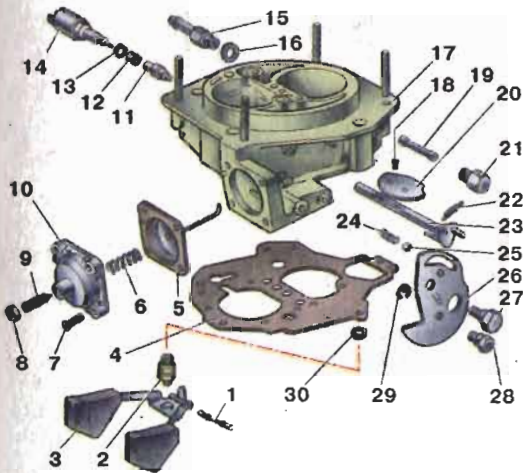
Детали крышки карбюратора мод. 2108: 1 – ось поплавков; 2 – топливный клапан; 3 – поплавок; 4 – прокладка крышки карбюратора; 5 – диафрагма пускового устройства; 6, 22, 24 – пружины; 7 – винт крепления крышки пускового устройства; 8 – контргайка; 9 – винт регулировки пускового зазора воздушной заслонки; 10 – крышка пускового устройства; 11 – топливный жиклер системы холостого хода; 12 – уплотнительное кольцо электромагнитного клапана; 13 – обойма уплотнительного кольца; 14 – электромагнитный клапан; 15 – штуцер подачи топлива; 16, 30 – уплотнительные шайбы; 17 – крышка карбюратора; 18 – винт крепления воздушной заслонки; 19 – топливный фильтр; 20 – воздушная заслонка; 21 – пробка; 23 – ось воздушной заслонки; 25 – шарик; 26 – рычаг управления воздушной заслонкой; 27 – ось рычага; 28 – шарнирная втулка крепления тяги привода воздушной заслонки; 29 – фиксатор
